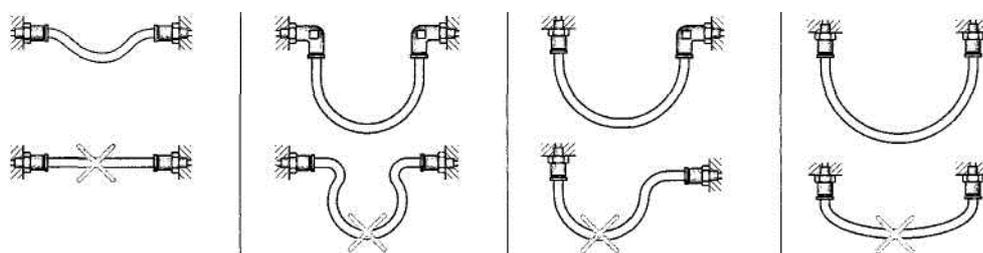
Монтаж гибких трубопроводов (шлангов)
